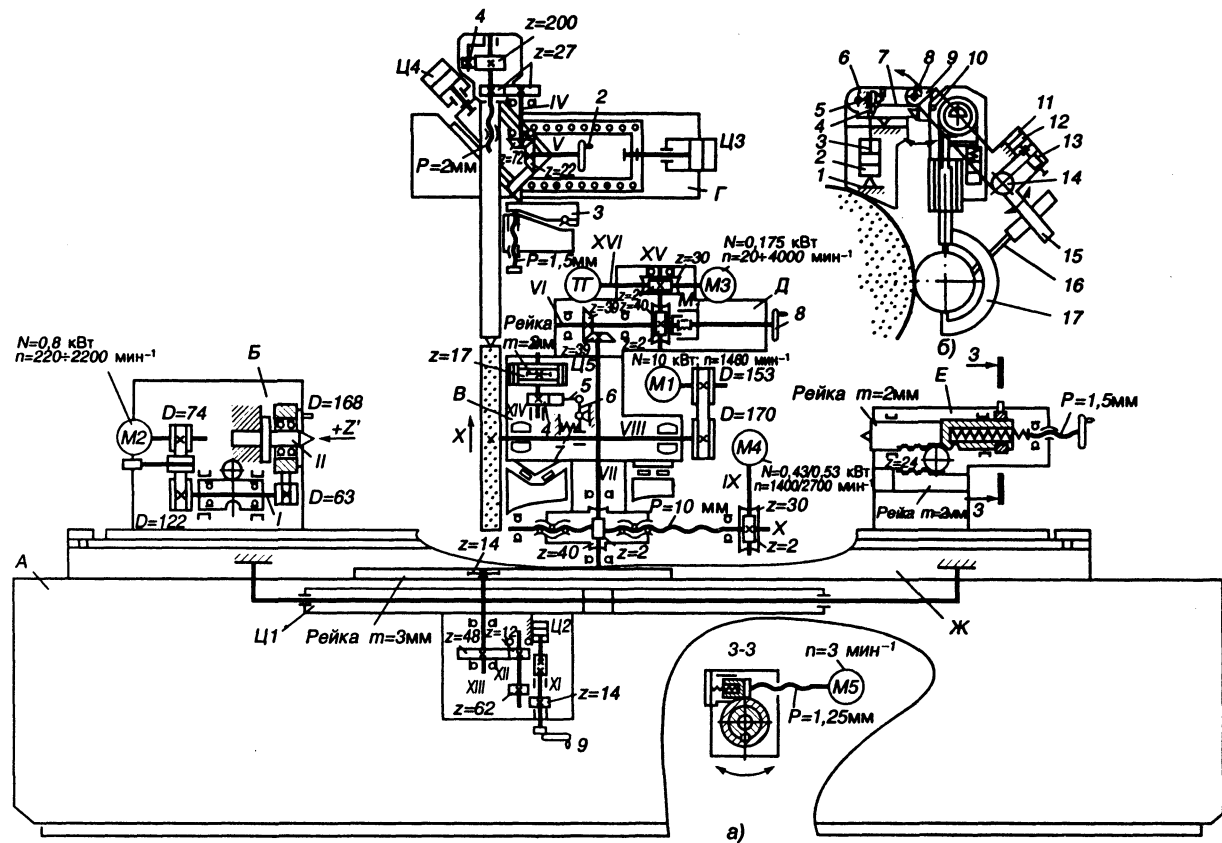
Круглошлифовальный станок 3М151Ф2 с ЦПУ:
